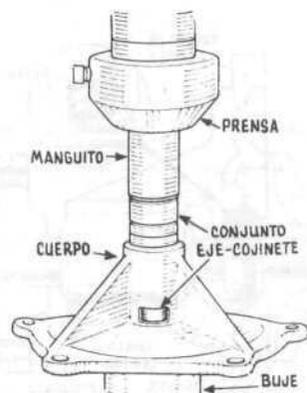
Montaje del eje y cojinete de la bomba de agua.
